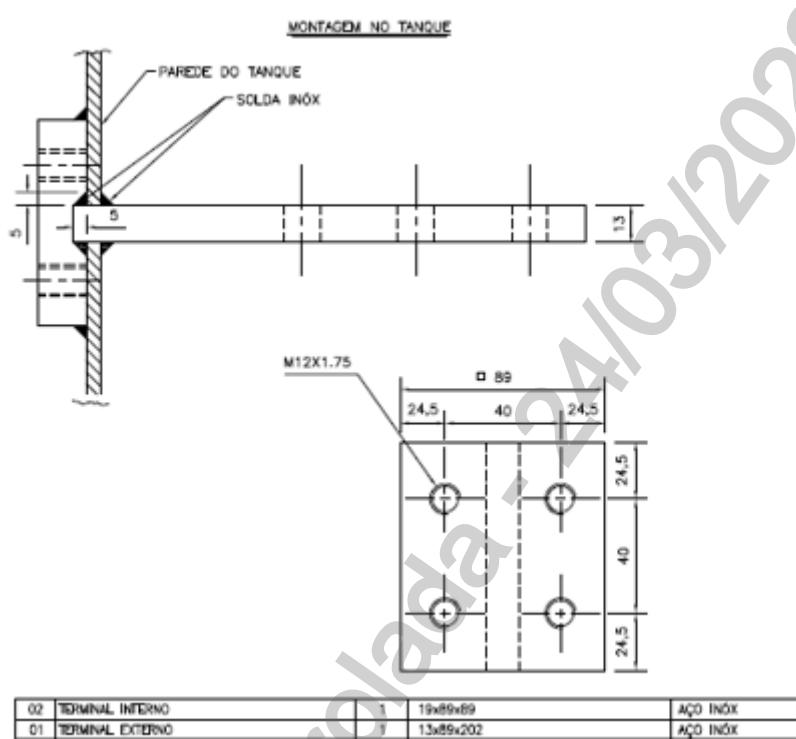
Detalhe do terminal de neutro soldado no tanque
